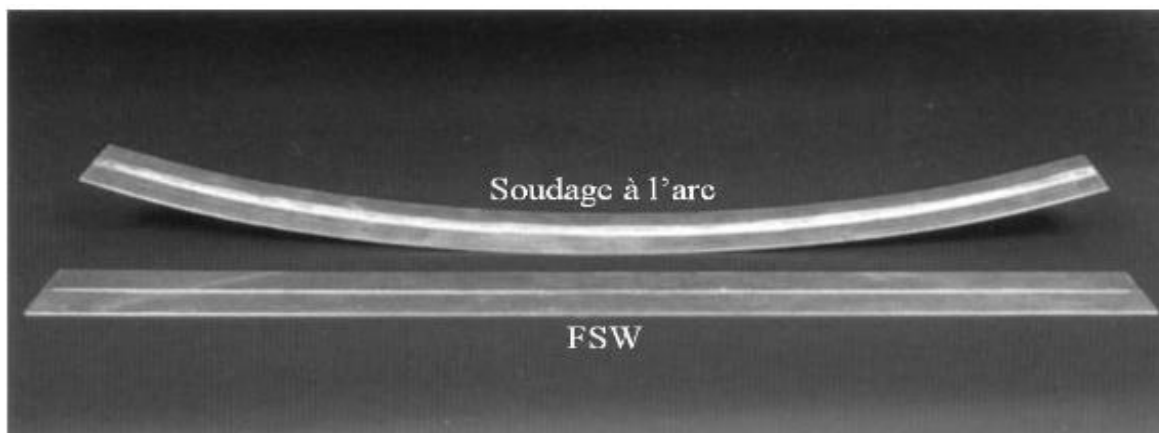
Comparaison de la distorsion entre le soudage FSW et le soudage à l'arc [9]
